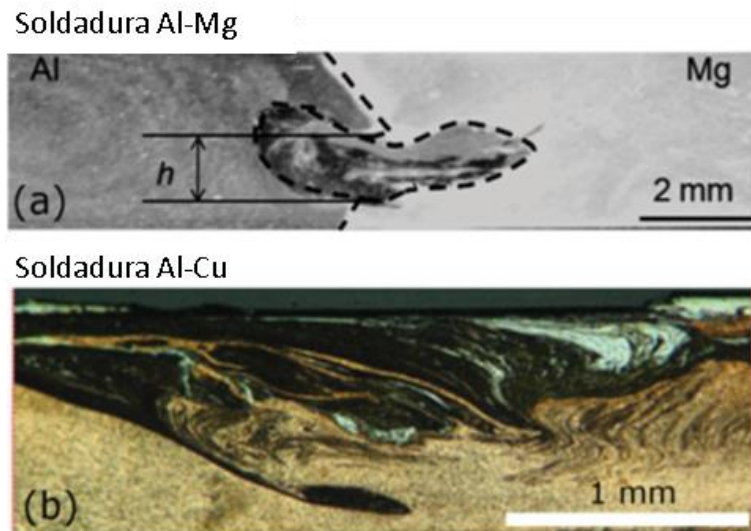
Flujo similar a un vórtice en (a) una soldadura Al 6063-Mg AZ31B y (b) una soldadura Al 5083-Cu DHP [41].
